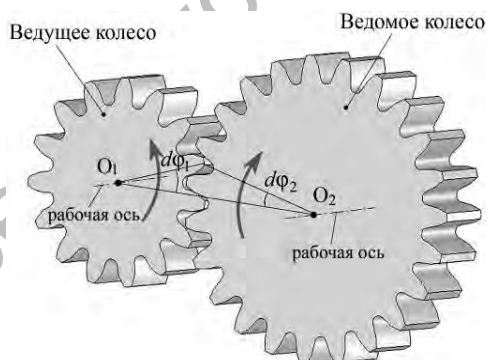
3D-модель зубчатой передачи и её кинематическая погрешность
